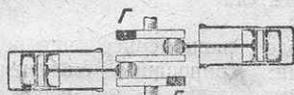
Двухцилиндровый горизонтальный двигатель с оппозитными противлежащими цилиндрами.
